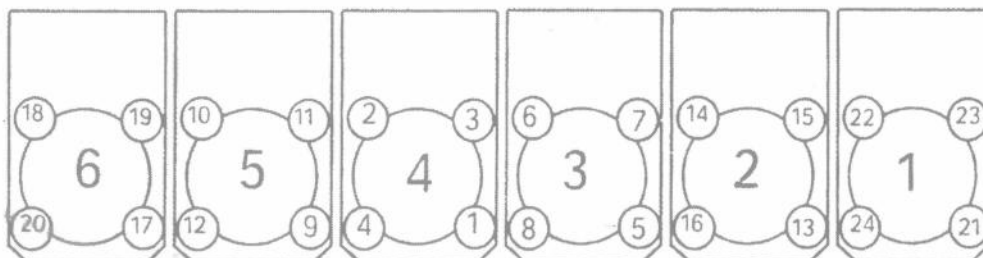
схема закручивающего порядка вторичной гайки главного болта головки цилиндра.
